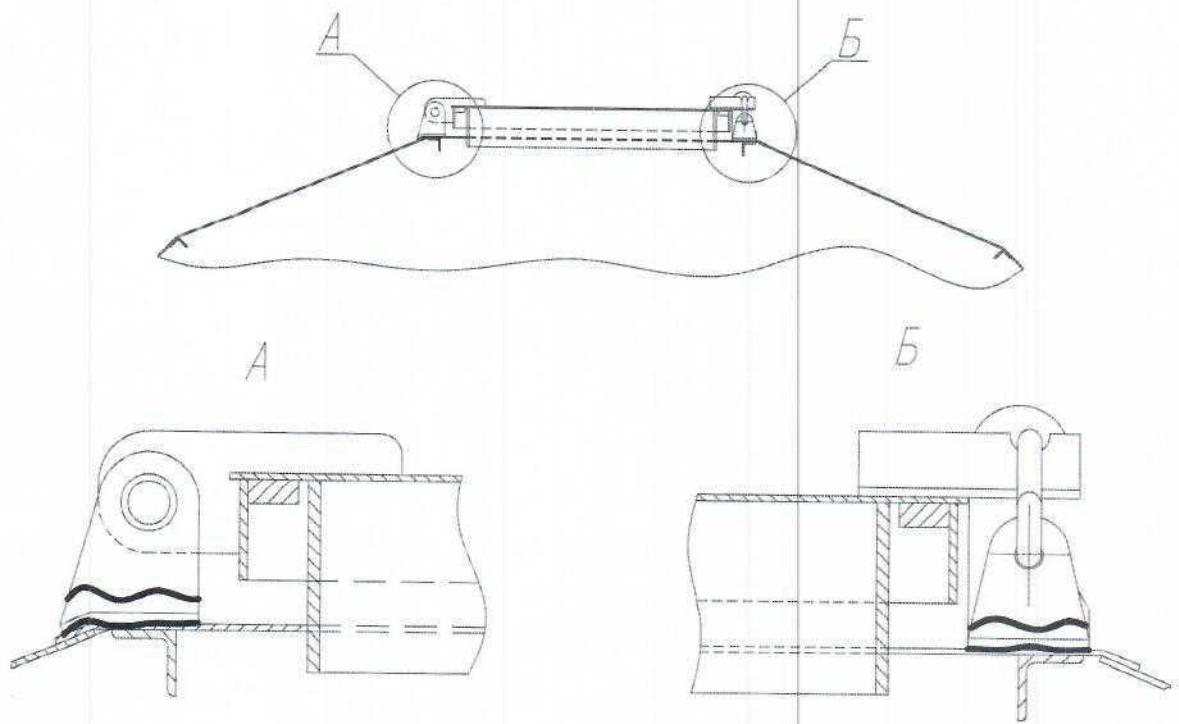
Трещины крепления крышки загрузочного люка
